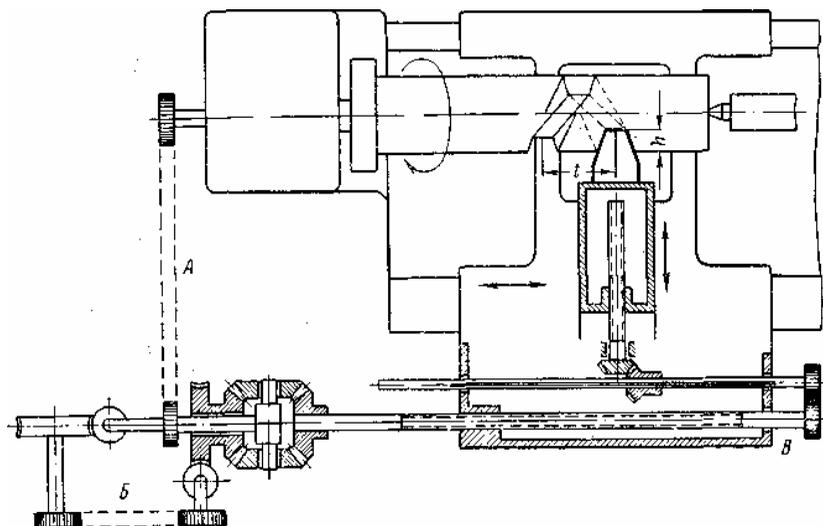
Компоновка станка для обработки винтов с переменным шагом
